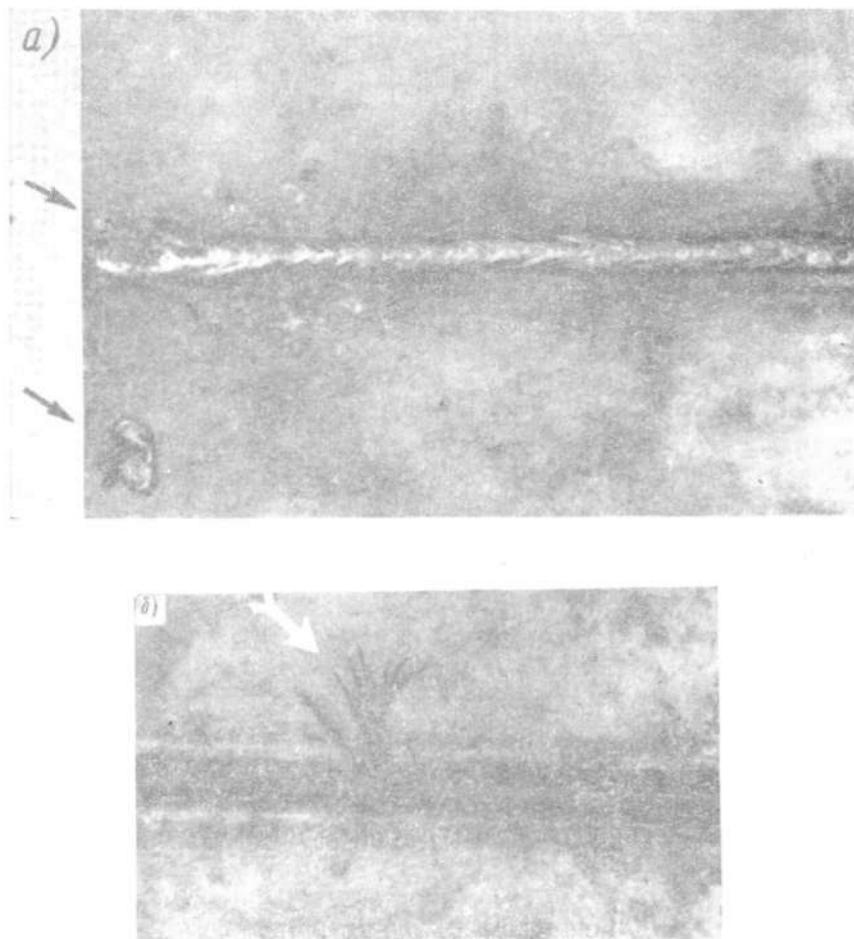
Вид сварного соединения, пораженного коррозией: а — точечная коррозия; б — коррозия под напряжением.
